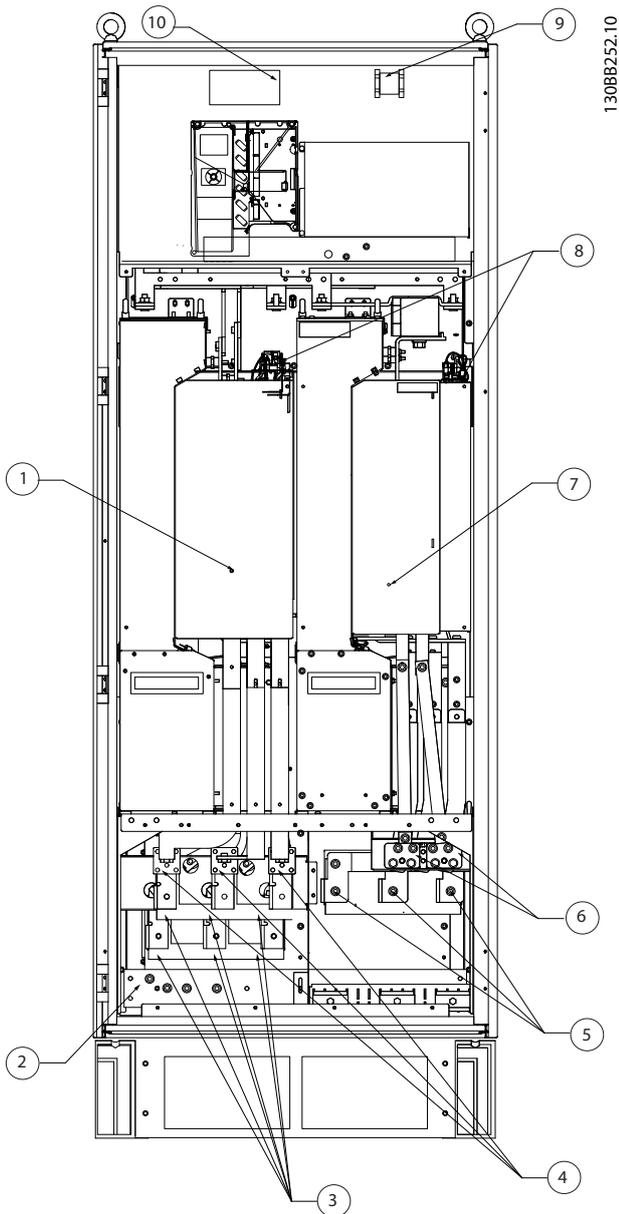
Шкаф выпрямителя и инвертора, типоразмеры F8 и F9
